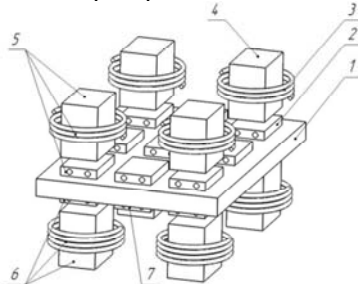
ЭМА преобразователь для контроля объектов с неравномерным покрытием 1 – объект контроля; 2 – плоский проводниковый излучатель; 3 – электромагнит; 4 – магнитопровод; 5 – основной магнитный узел; 6 – дополнительный магнитный элемент; 7 – дополнительный плоский проводниковый излучатель.
